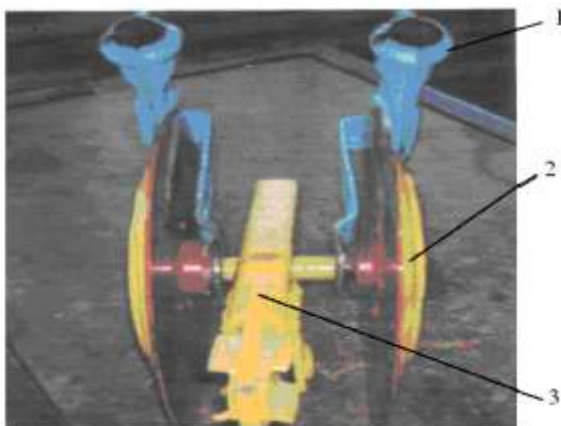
Двухдисковый сошник с односторонними ребрами-бороздкообразователями (вид спереди): 1 – корпус сошника; 2 – реборды-бороздкообразователи; 3 – семянаправитель
